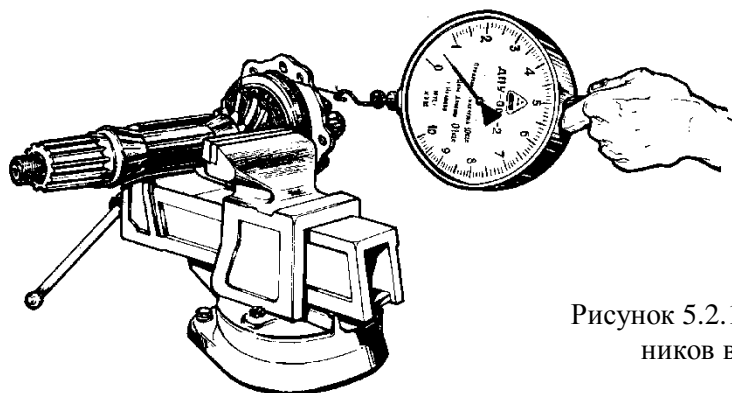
Проверка регулировки подшипников ведущей конической шестерни
